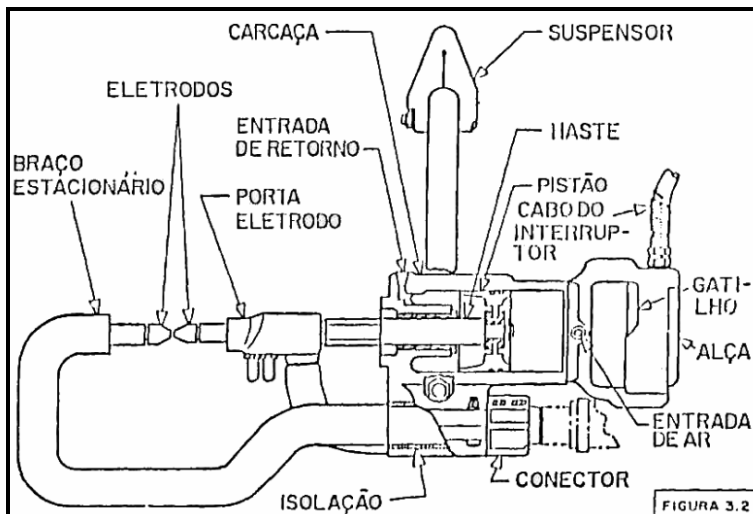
MAQUINA DE SOLDA TÍPICA
